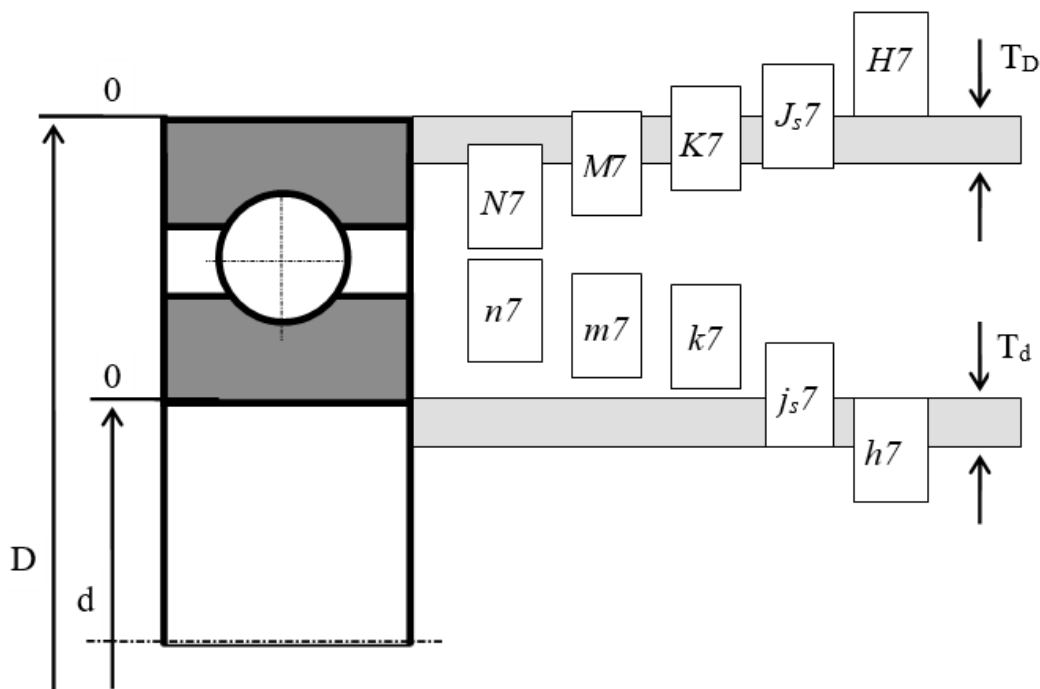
Расположение полей допусков размеров подшипника
